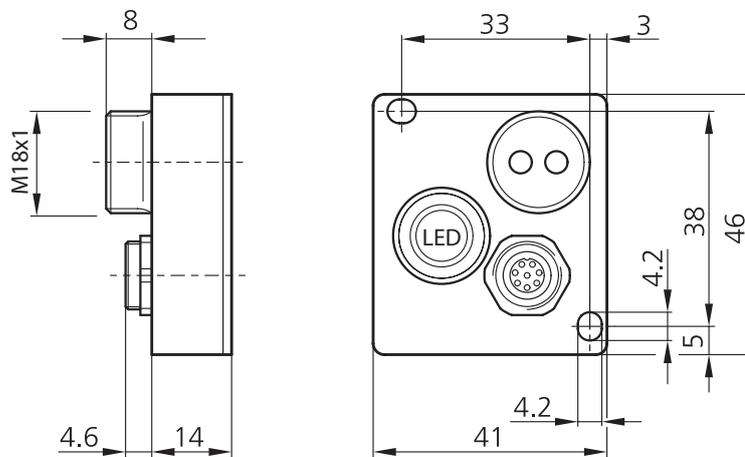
, Maßzeichnung / Figure 2, Drawing
